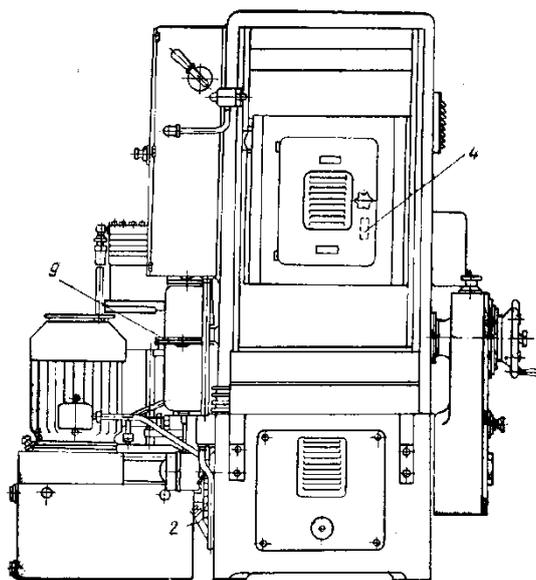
Типовая карта смазки плоскошлифовального станка (3А 741)
